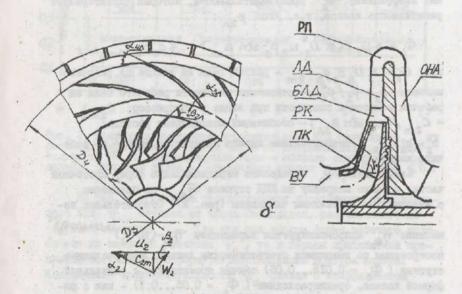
Рис. I. Основние элементи проточной части и резчетние сечения ступени центробежного компрессора осерадиального (а) и раде-ального (б) типов: ВУ — вкодное устройство; ПА — подкручиварщий аппарат; БУ — заборное устройство колеса; РК — рабочее колесо; БП — безлопаточний дифузор; РЛД — радиальный лопаточний дифузор; РОП — радиальный поворот; ОСА — осевой спримляющий аппарат; ОНА — обратный направляющий аппарат; У — сборная улитка; ПК — покрывной диск рабочего колеса; 2Р — решетии второго рада
